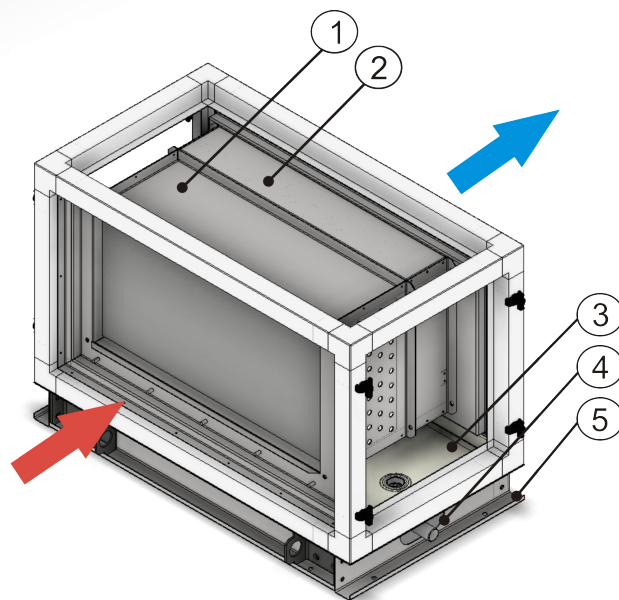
Widok wnętrza sekcji bazowej i jej wyposażenia.
